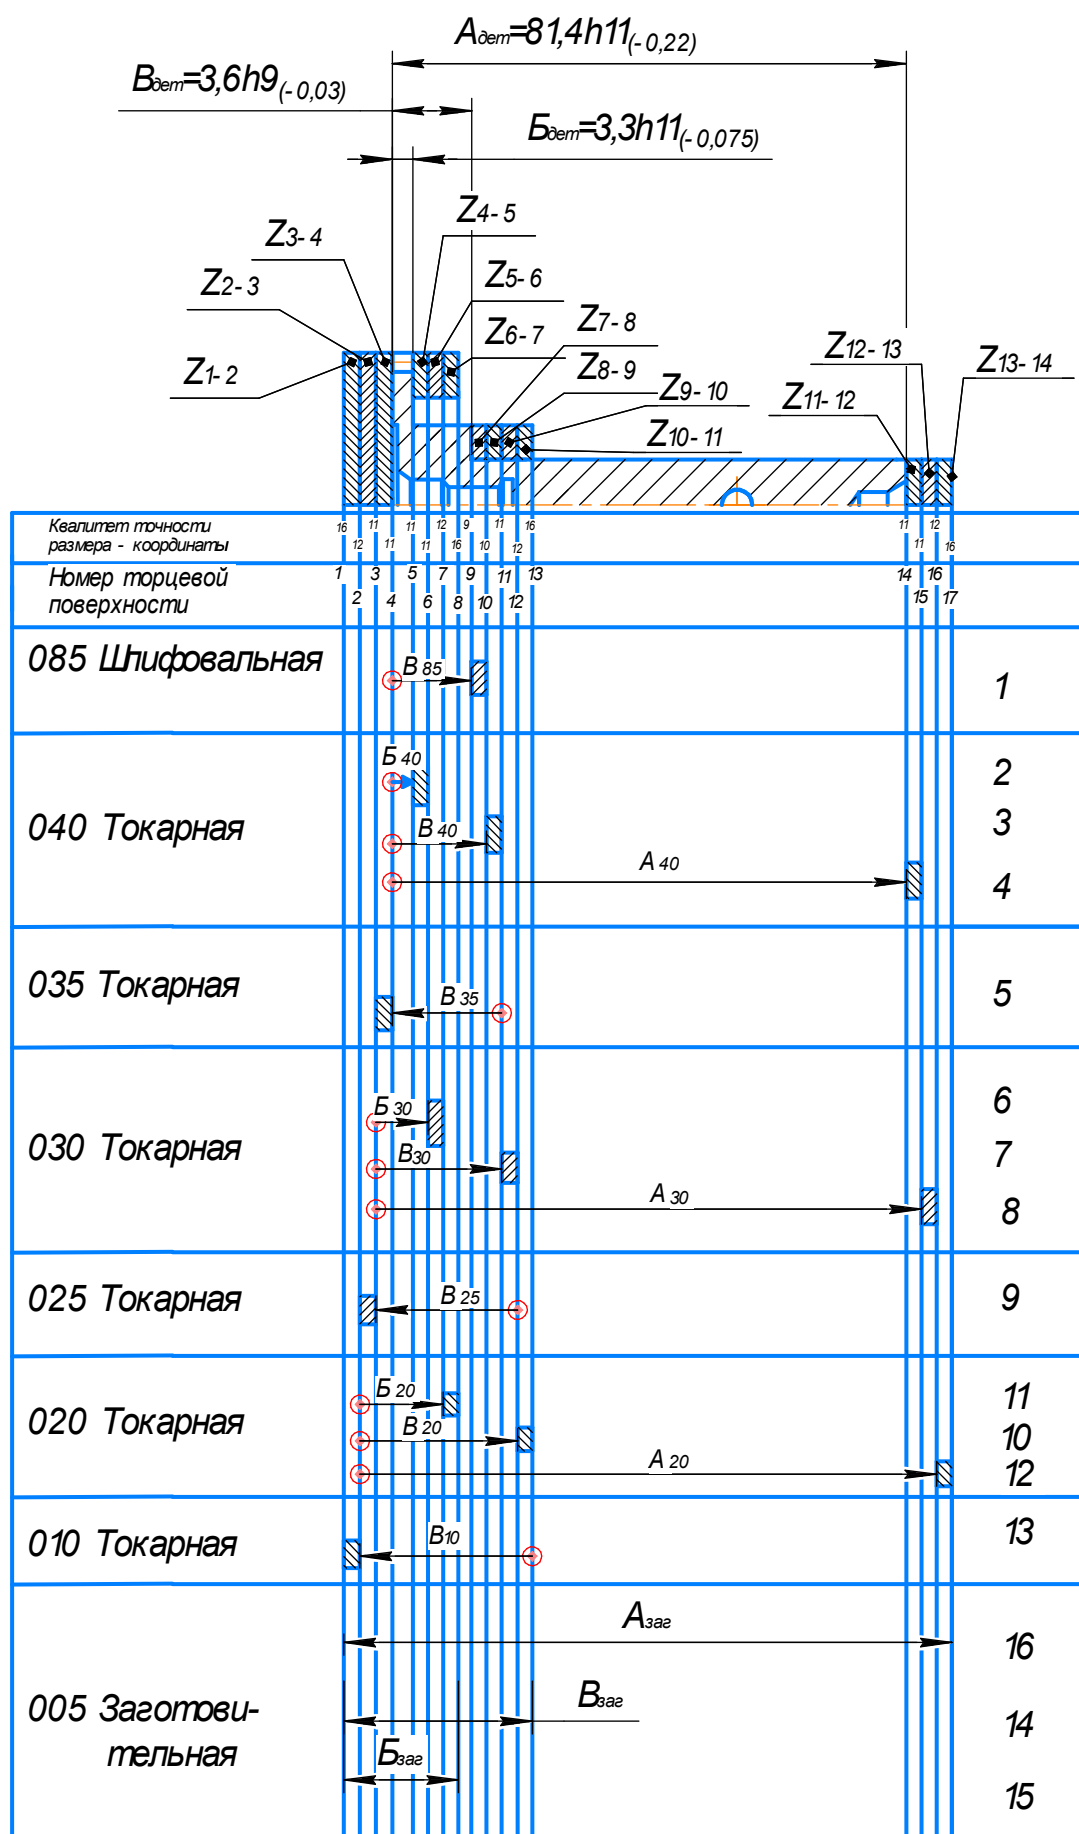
Розмірна схема формоутворення торцевих поверхонь
